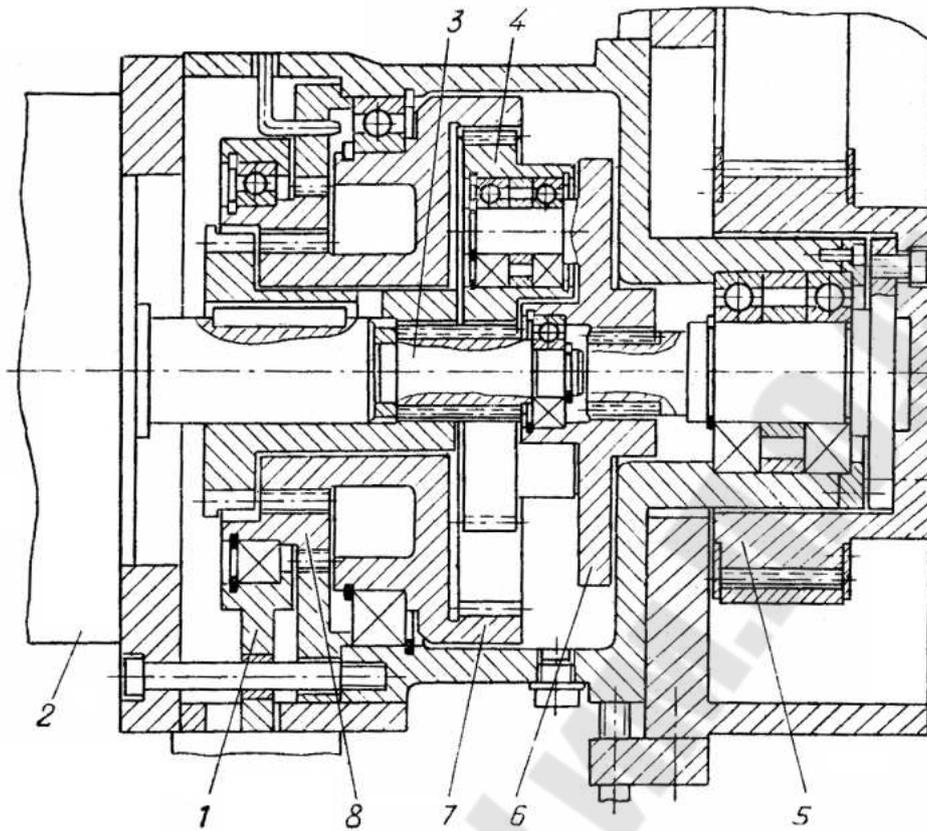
Конструкция двухступенчатой планетарной коробки скоростей:
